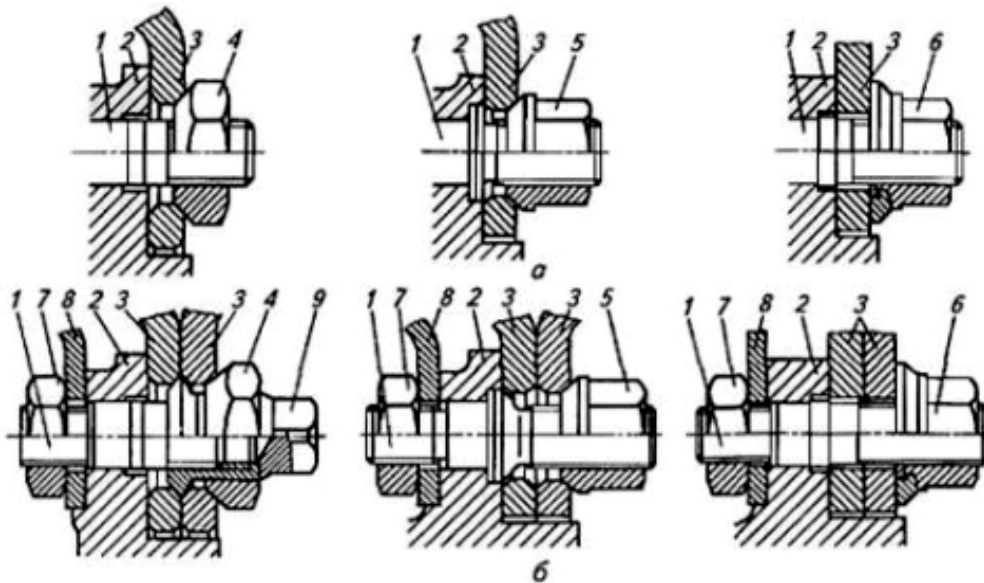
Крепление дисковых колес грузовых автомобилей: а - одинарных; б - сдвоенных; 1 - шпилька; 2 - ступица; 3 - диск; 4 - гайка крепления наружного диска; 5 - гайка типа ДИН; 6 - гайка с завальцованной шайбой; 7 - гайка крепления тормозного барабана; 8 - тормозной барабан; 9 - гайка крепления внутреннего диска
